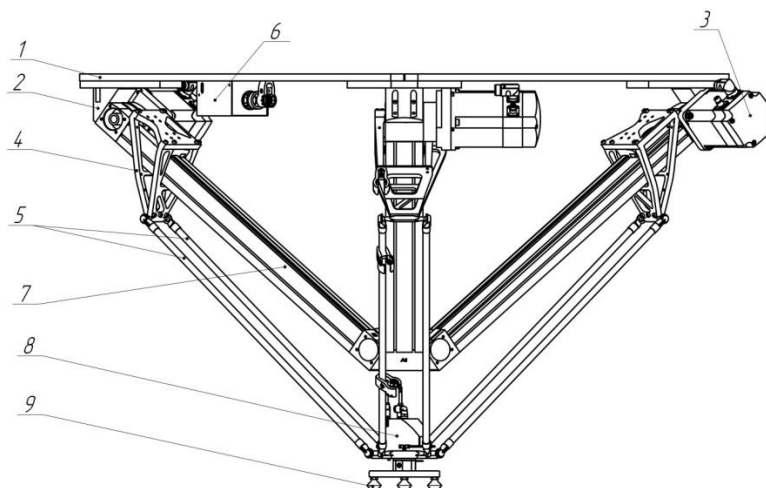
Конструкція робота-трипода: 1-каркас; 2-монтажні кронштейни; 3-серводвигун; 4-монтажний блок; 5-пара тяг; 6-корпус інтерфейса; 7-привод із зубчастим ременем; 8-монтажна плита для кріплення захвату; 9-вакуумна присоска.
